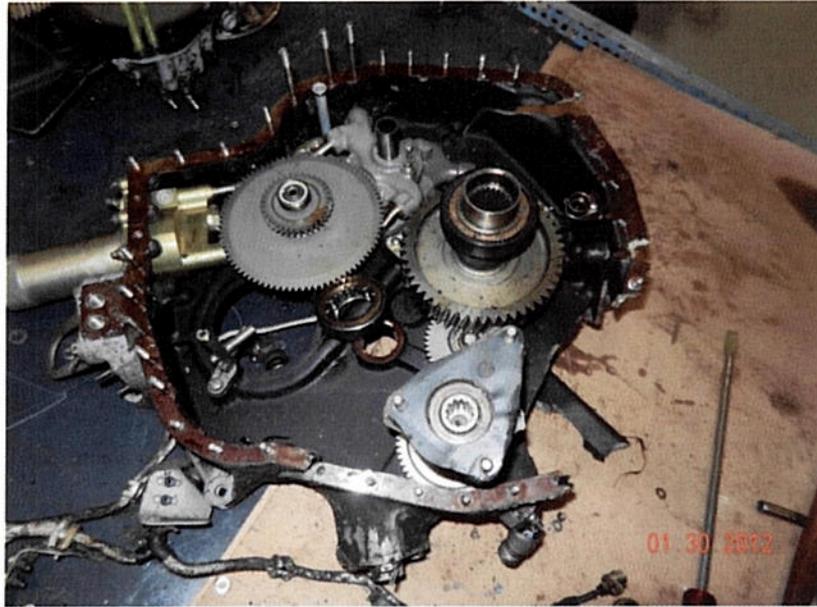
Caja de accesorios con engranajes en buen estado.
